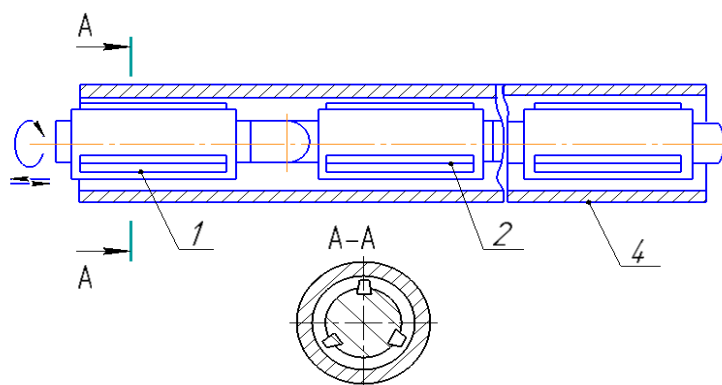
Конструкция индуктора на постоянных магнитах с их параллельным расположением: 1 – каркас из немагнитного материала; 2 – постоянные магниты; 3 – ферроабразивный порошок; 4 – обрабатываемая деталь
